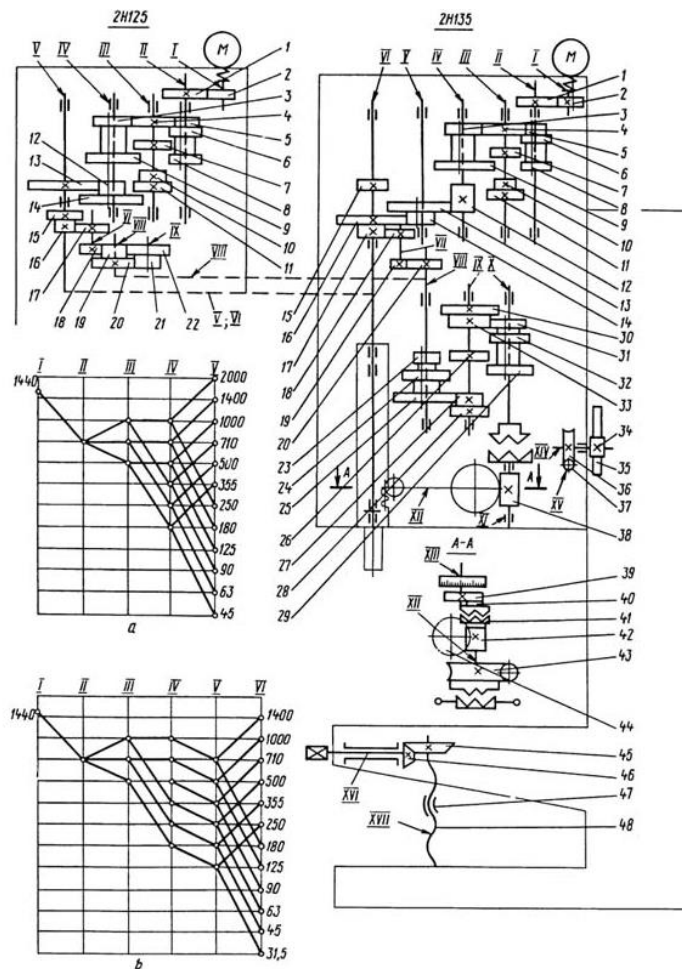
Кінематична схема приводу головного руху верстата
